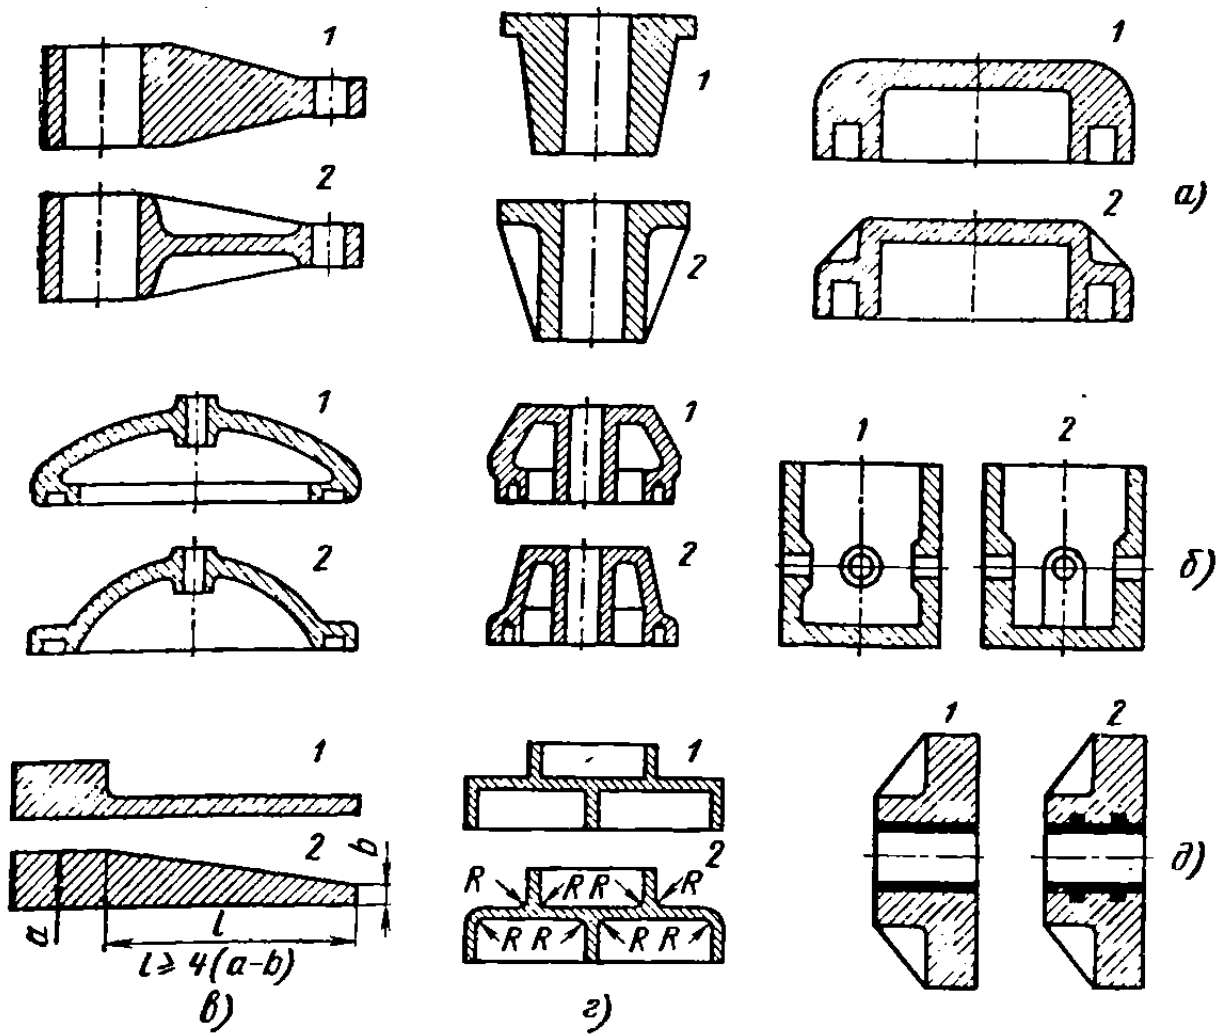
Схема выполнения элементов конструкции отливок:
